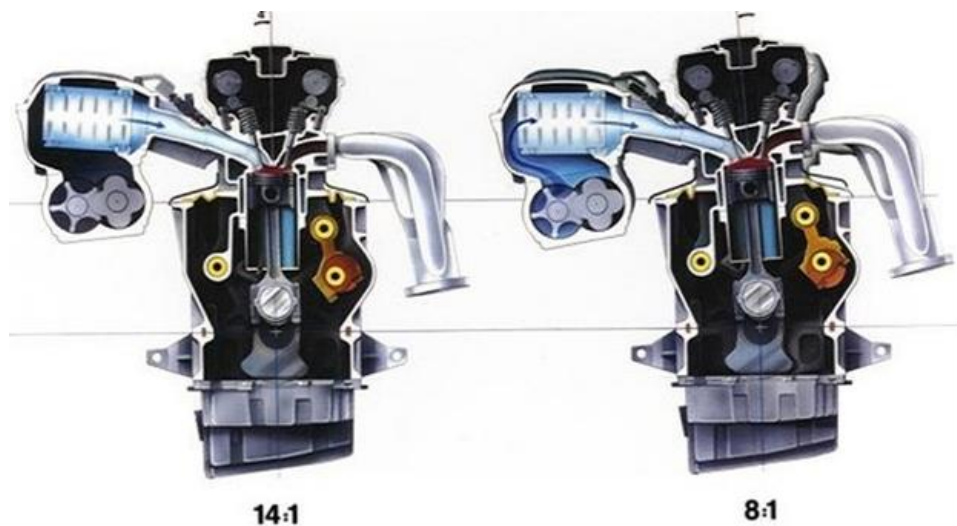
Variabilní klikový mechanismus motoru VC-T (Infiniti); větší kompresní poměr (vlevo), menší kompresní poměr (vpravo) [34].
